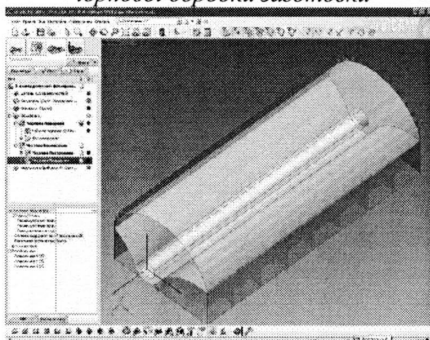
Заготовка перед моделюванням чорнової обробки
